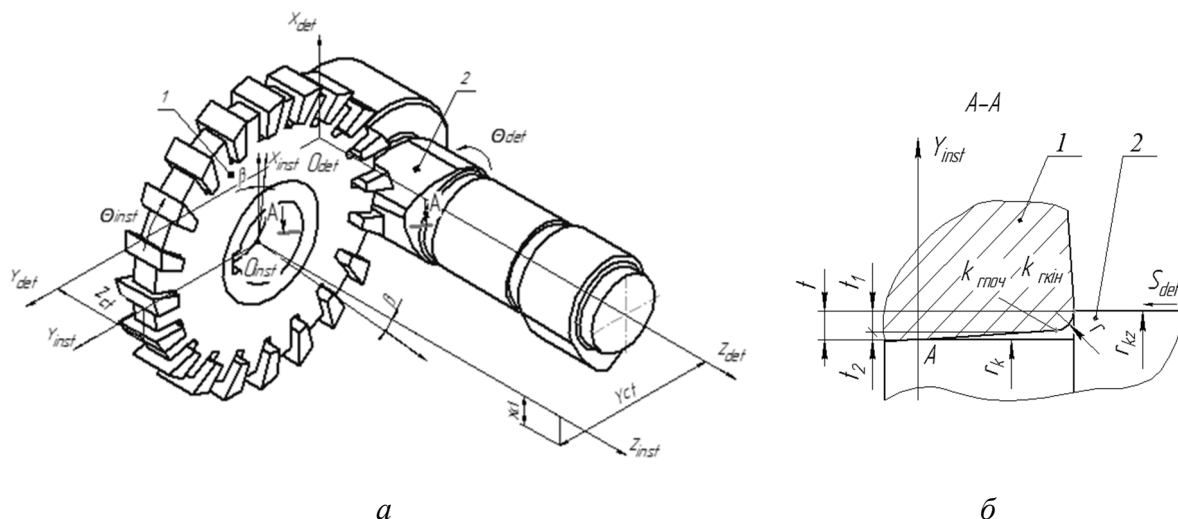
Схема фрезерування розподільного вала зі схрещеними осями інструмента та деталі
